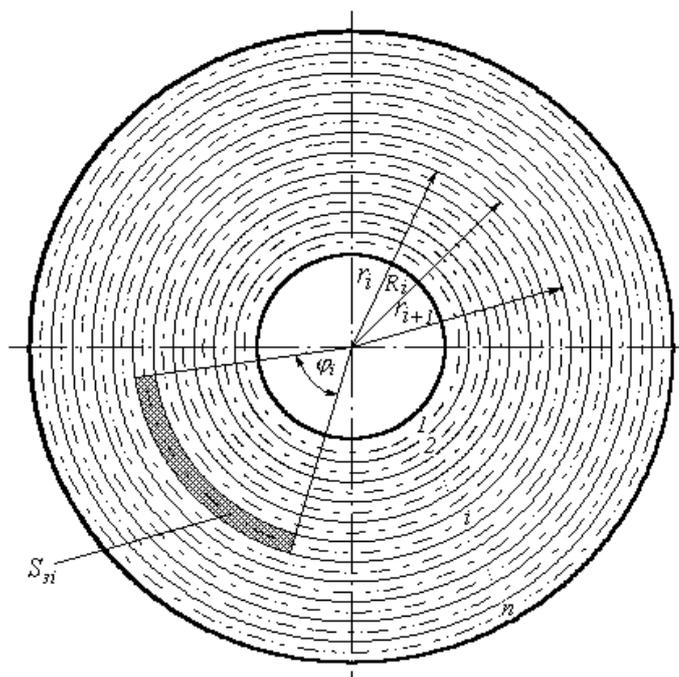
Схема розбивки поверхні плоского притира на умовні кільцеві елементарні зони
